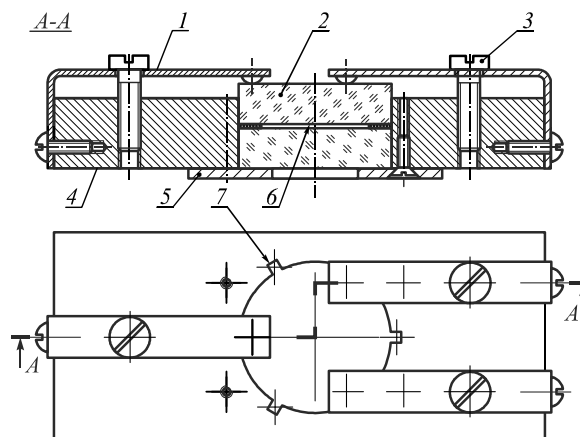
Конструкция интерферометра: 1 – прижимные «лапки», 2 – зеркала, 3 – регулировочный винт, 4 – корпус крепления интерферометра, 5 – прижимная пластинка, 6 – воздушный зазор между зеркалами, 7 – отверстие для установки пьезоэлемента
